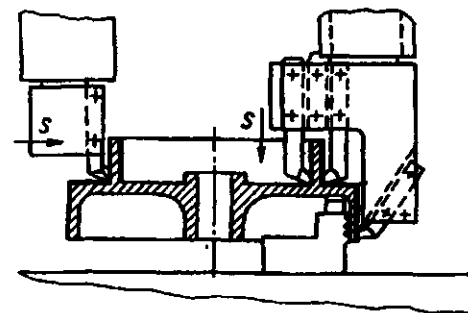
Схема многоинструментной обработки крупногабаритной заготовки
